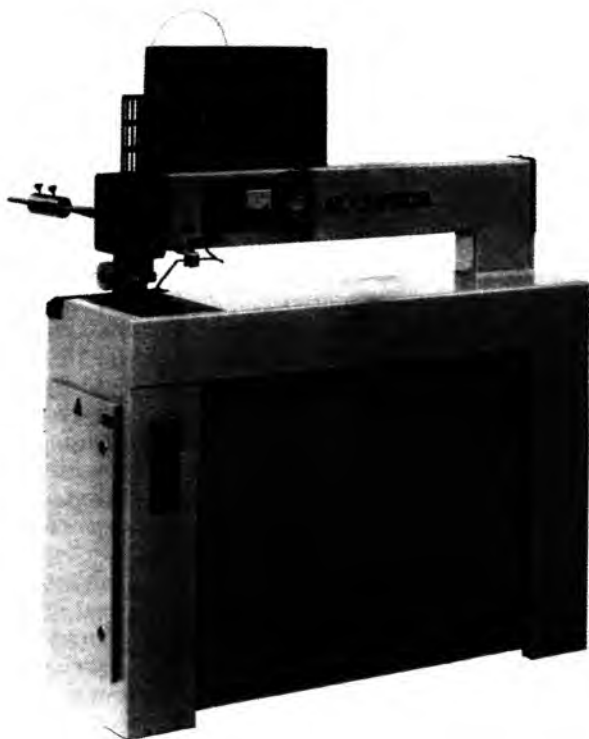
Общий вид станка Кирег для соединения полос шпона клеевой нитью способом "зиг-заг"
